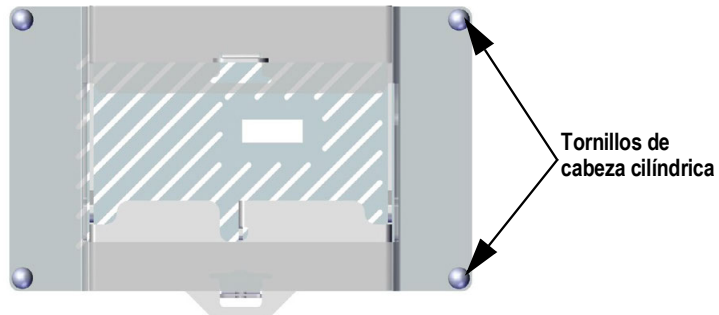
Posición de los tornillos en el soporte del carril DIN
